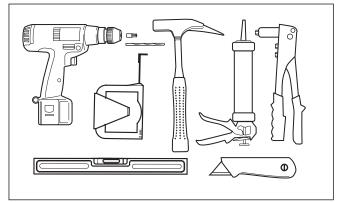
Montage-Werkzeuge: Wasserwaage, Akku-Schrauber,
